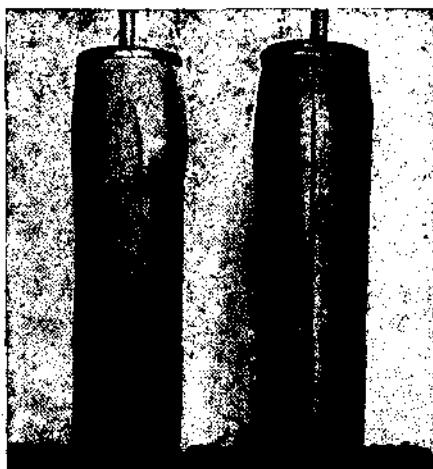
Цилиндр, испытанный под давлением свыше 20 атм., лопнул не на месте шва.
